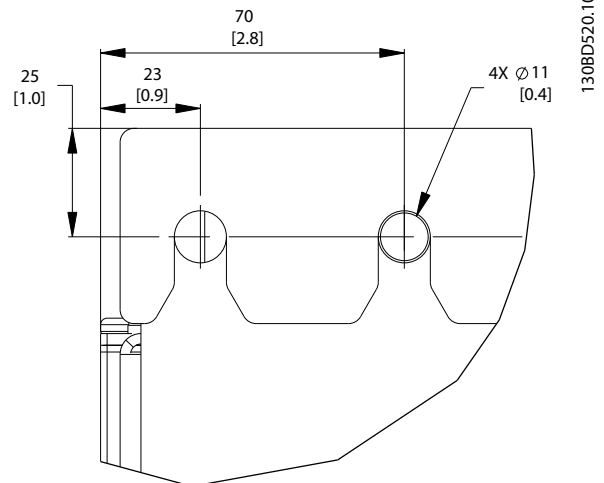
Детальный чертеж верхнего монтажного отверстия, D7h
